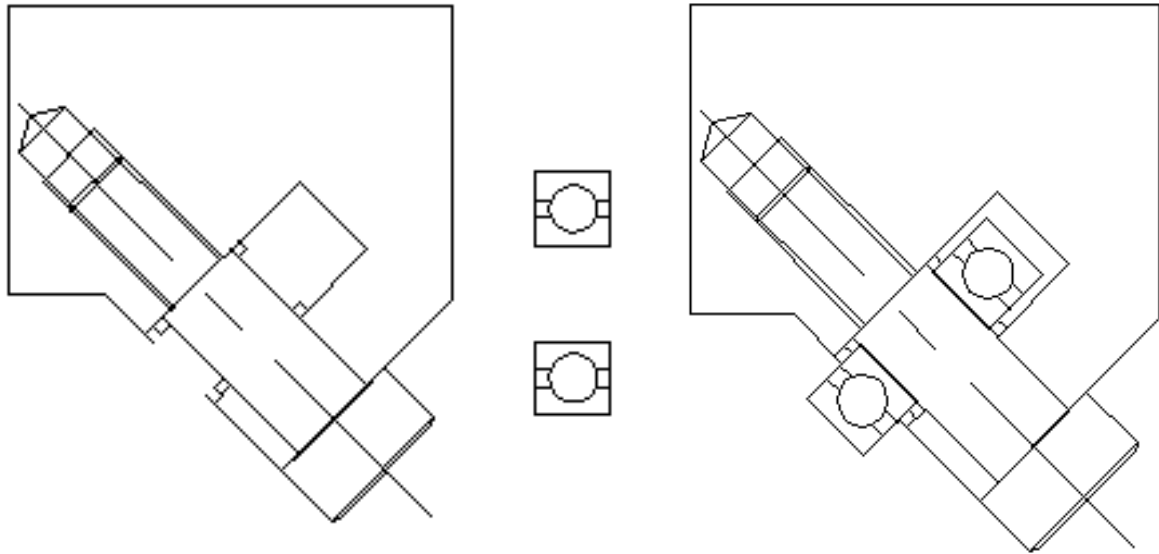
Фиксатор (исходный и конечный чертеж)
